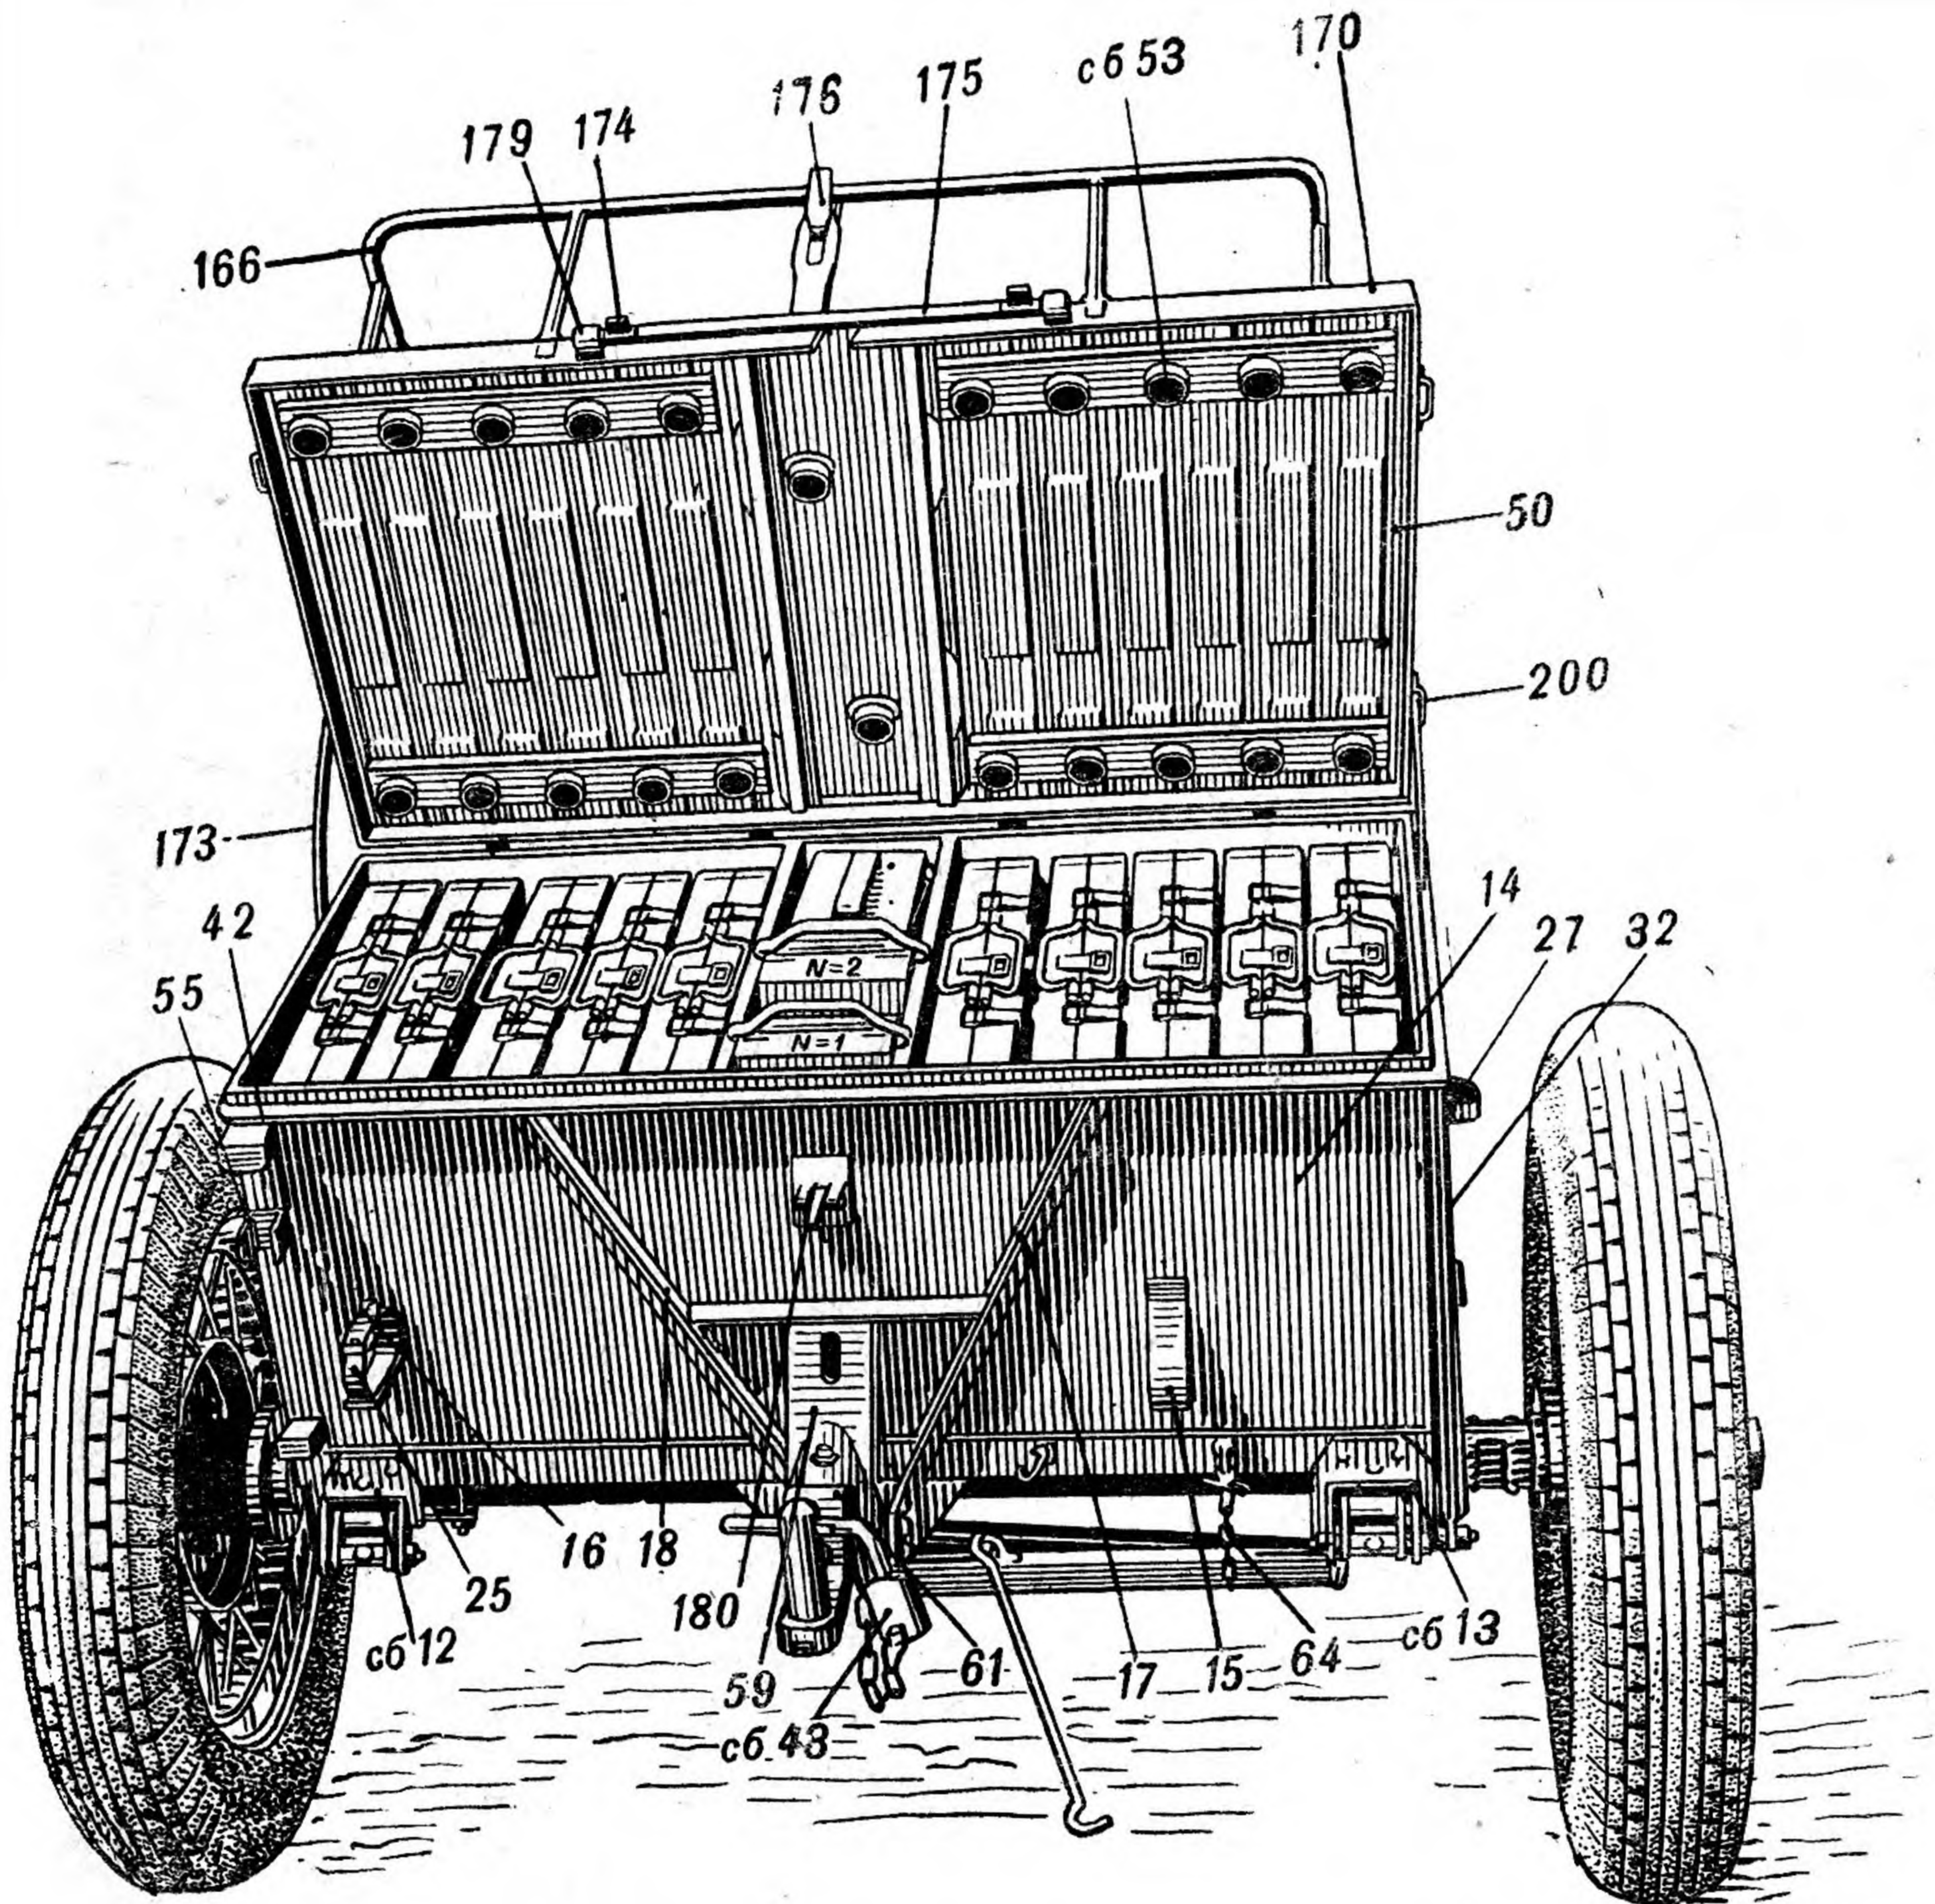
Универсальный ход (вид сзади с открытой крышкой)
